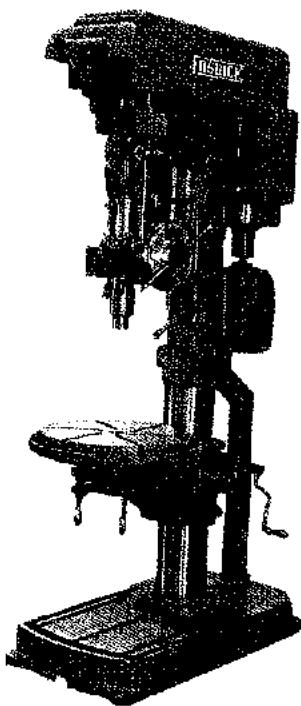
Taladradora vertical corriente con transmisión por engranajes (Fosdick Machine Tool Co.)
